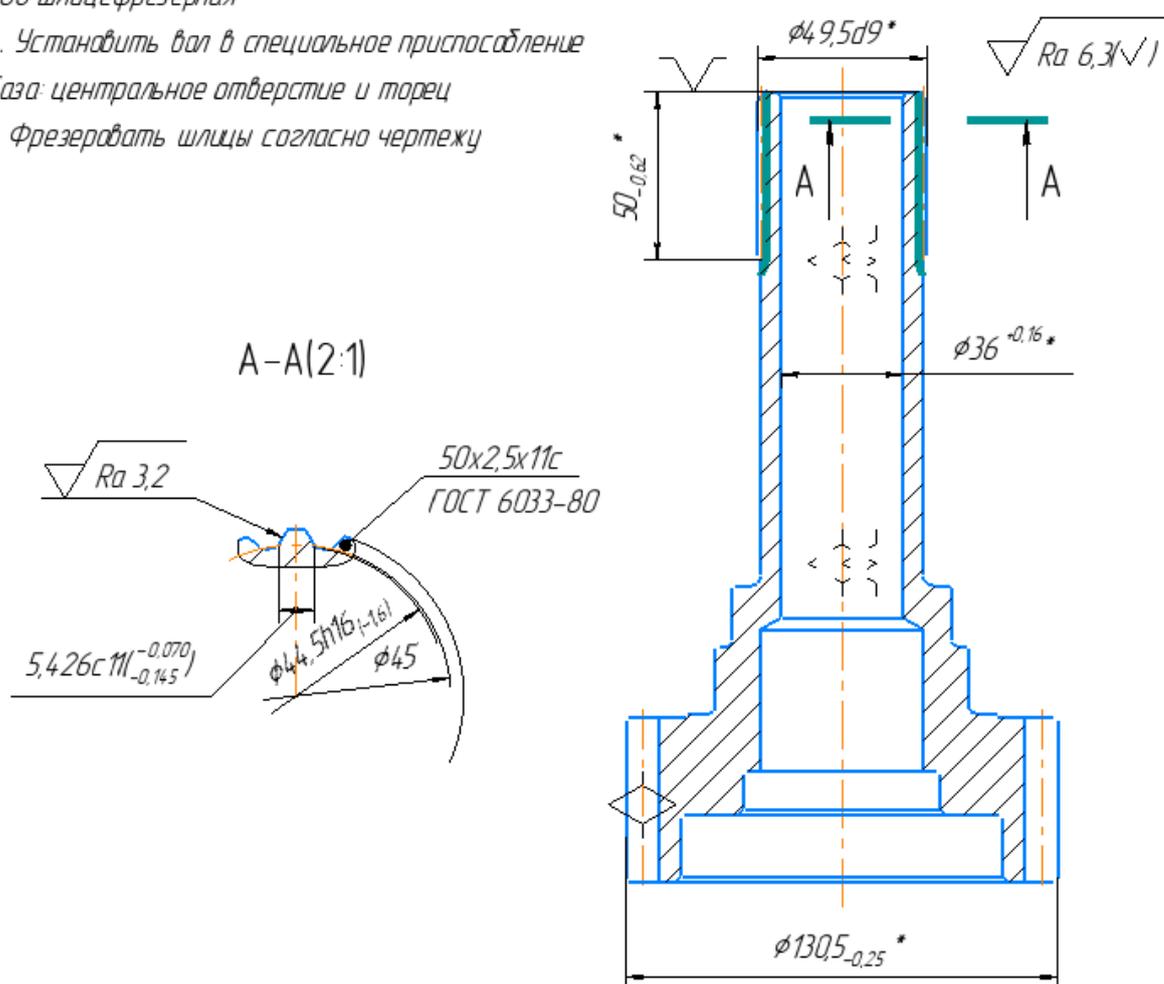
Схема базирования детали на операции 060 Шлицефрезерная
